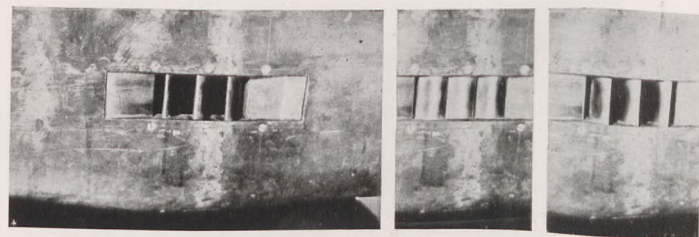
Schöpfflügel in den Außenhautöffnungen der Stampftanks.
